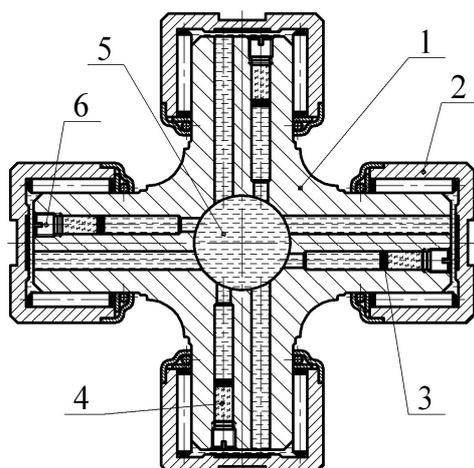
Крестовина карданного шарнира с автоматической системой смазки: 1 – крестовина; 2 – игольчатые подшипники; 3 – поршни; 4 – наполнитель; 5 – смазочный материал; 6 – заглушки
